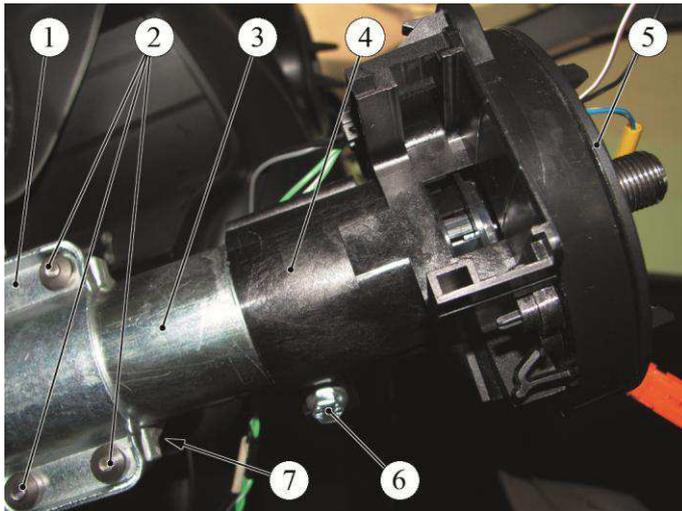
Снятие соединителя и выключателя зажигания:
